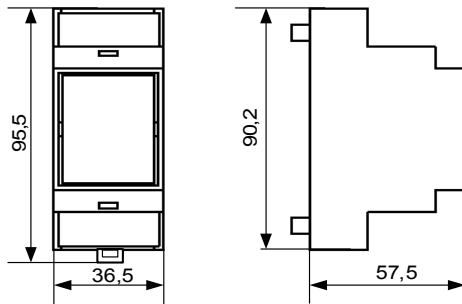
Габаритные и присоединительные размеры преобразователя
